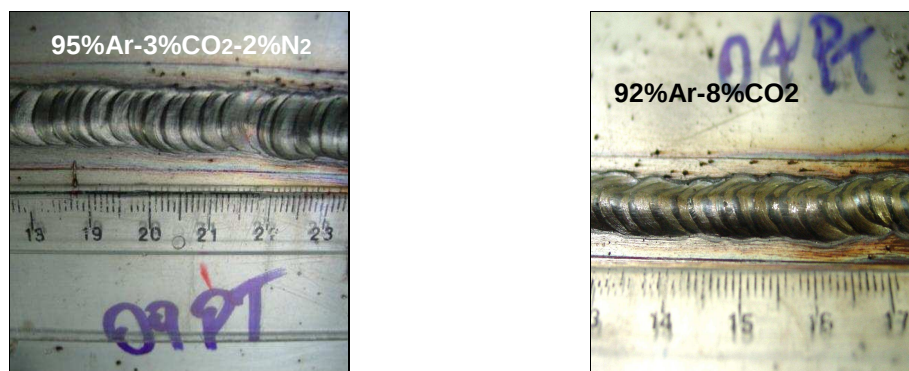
Aspecto do cordão de solda – MAG-PT com *stickout* de 15 mm
